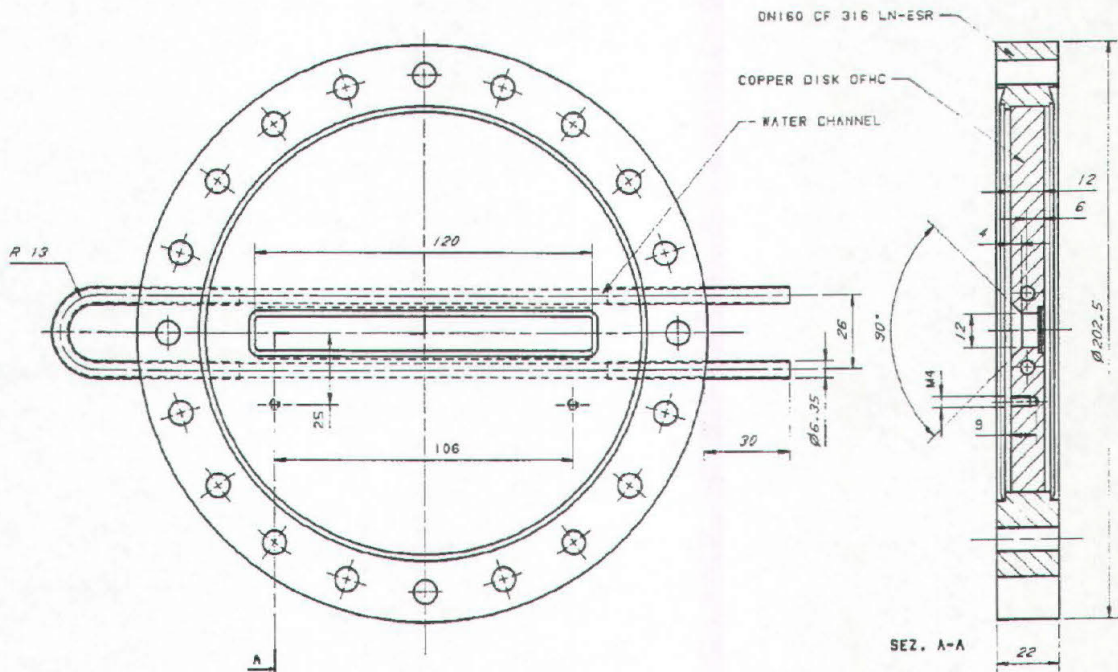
Prospetto e sezione della prima finestra di berillio.
